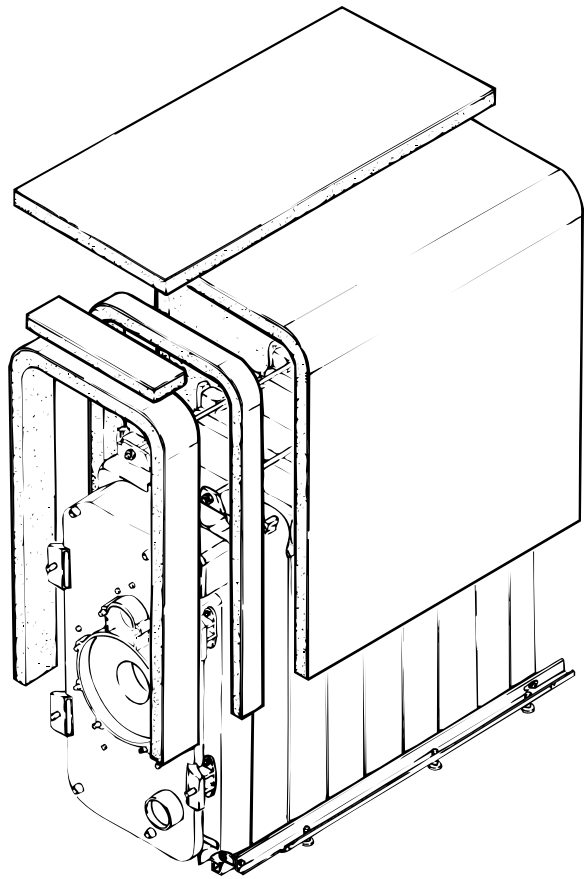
Ecksäulen und Winkelrahmen befestigen.
